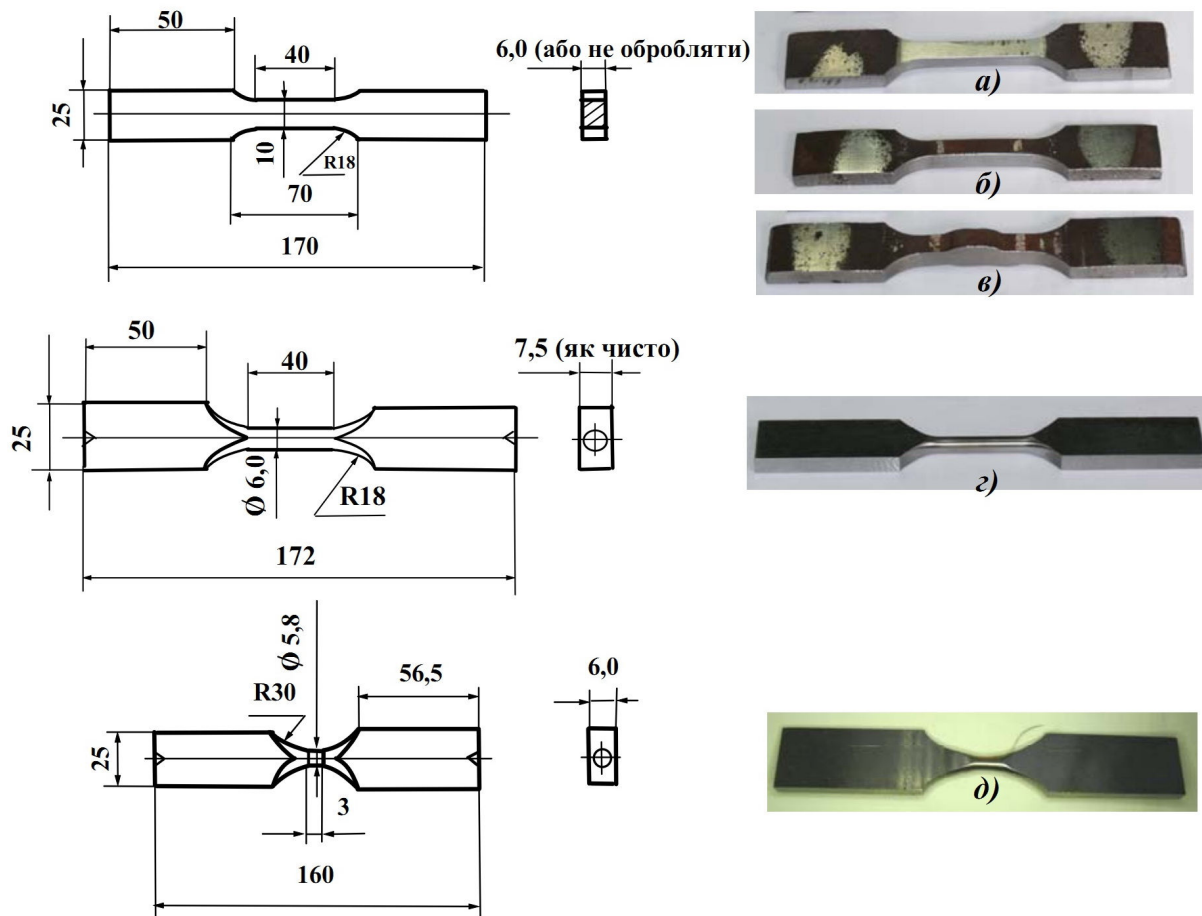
Креслення та зовнішній вигляд зразків для випробувань на розтяг: а) зразок з обробкою поверхні робочої частини; б) зразок із ОМ без обробки поверхні робочої частини; в) зразок зі зварним з'єднанням (з поздовжнім заводським швом) без зняття підсилення шва; г) повномірний циліндричний зразок; д) циліндричний зразок із вкороченою робочою частиною
